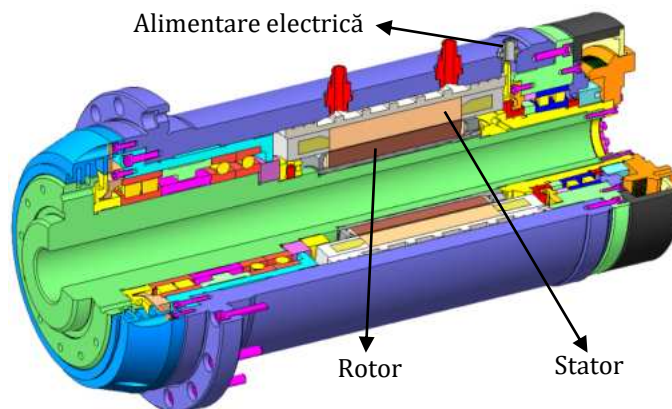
Motor integrat în AP pentru m-u CNC
